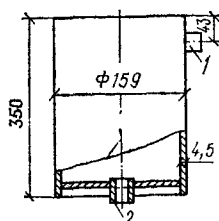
Вертикальный непроточный воздухоотборник ВС-3
